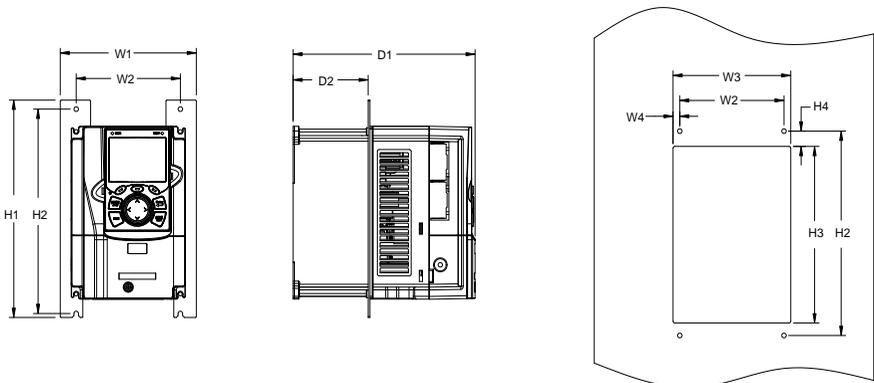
1R5G/2R2P-075G/090P Flanschmontage
